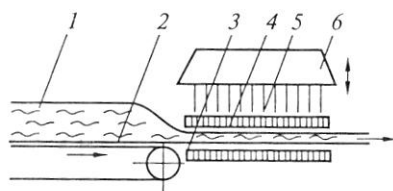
Схема получения нетканого полотна иглопробивным способом: 1 – холст; 2 – транспортирующая лента; 3 – прокладочный стол; 4 – очистительный стол; 5 – иглы; 6 – игольная доска
